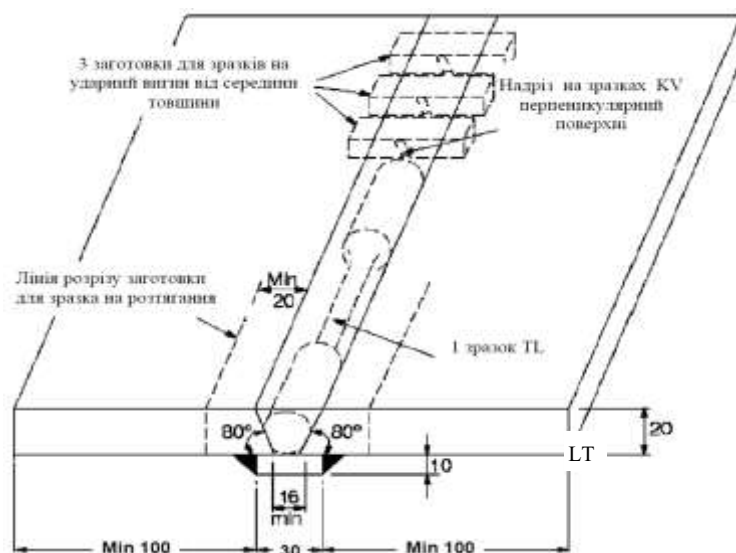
Проба наплавленого металу при випробуваннях електродів для ручного дугового зварювання.
